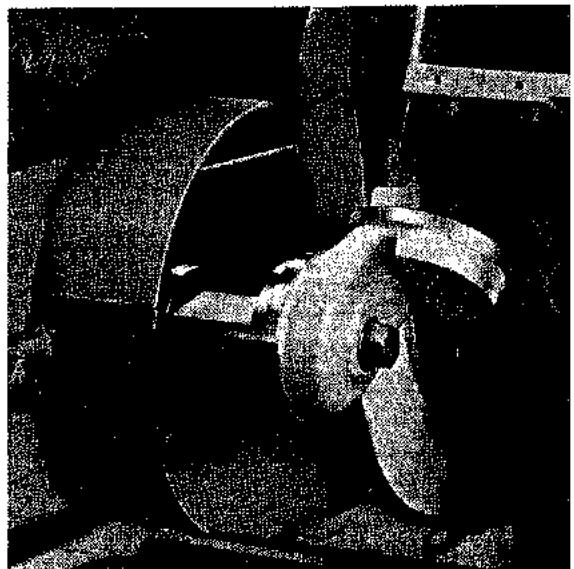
Rectificado de penetración (Cincinnati Milling Machine Co.)
